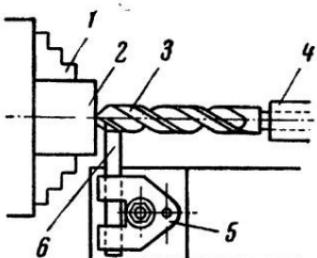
Точное засверливание с поддержкой сверла упором: 1 — кулачки патрона; 2 — обрабатываемая деталь; 3 — сверло; 4 — пиноль задней бабки; 5 — резцедержатель; 6 — пластиинка-упор.
